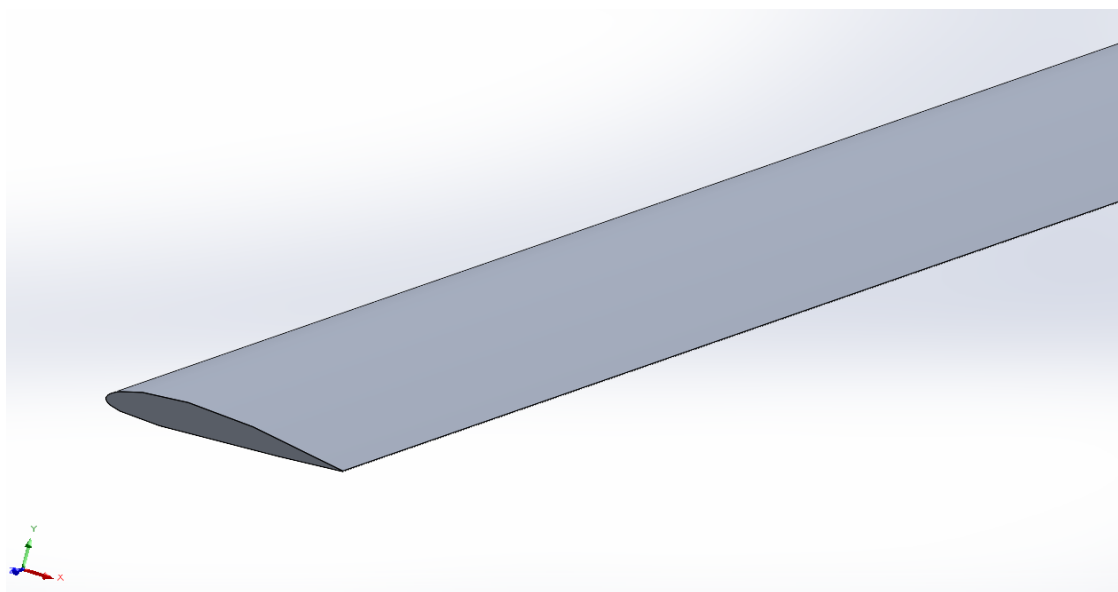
Vista del perfil alar NACA 2412 extruido 200 mm en SolidWorks
